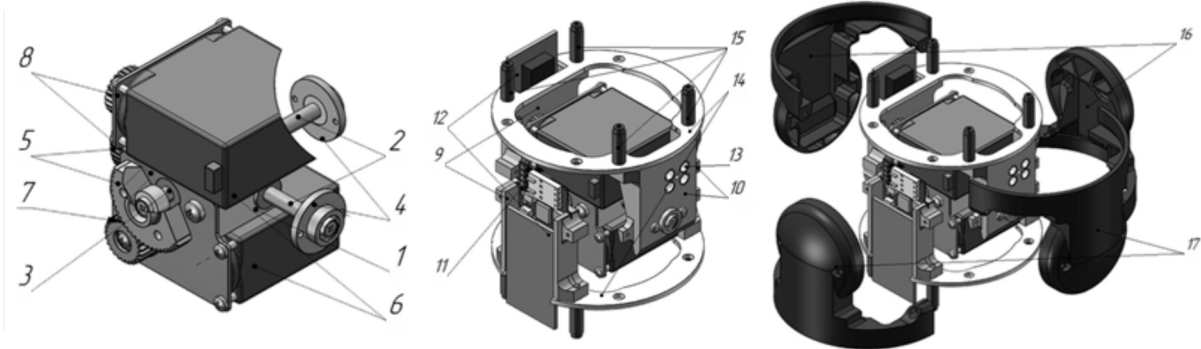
Корпус шарнира и корпус с установленными кронштейнами с фланцами
